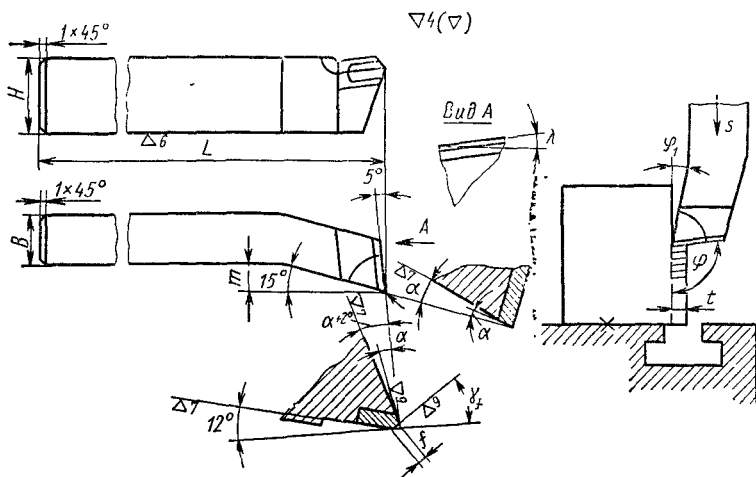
Левый подрезной строгальный резец с пластинкой твердого сплава
